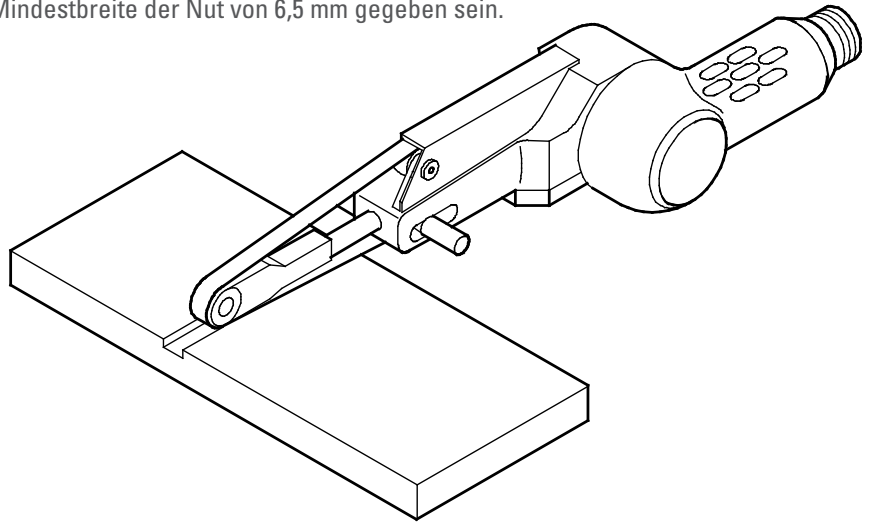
Nuten bearbeiten (Symbolzeichnung)
